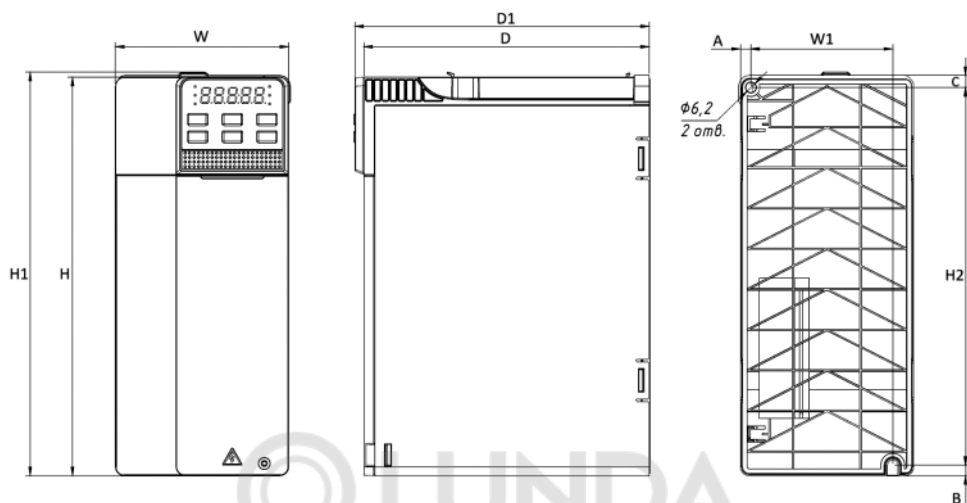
Чертеж преобразователя частоты типоразмера С3
